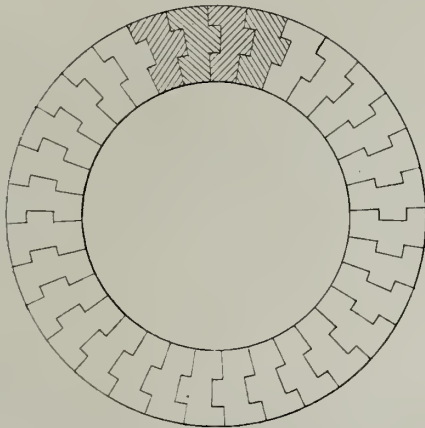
Coupe de l'électrode Siemens et Halske.
